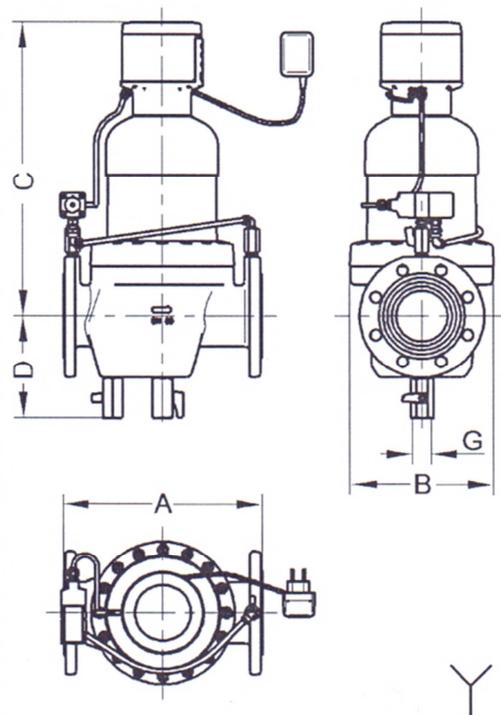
Medidas de montaje JPF-A DN 65 – 100
